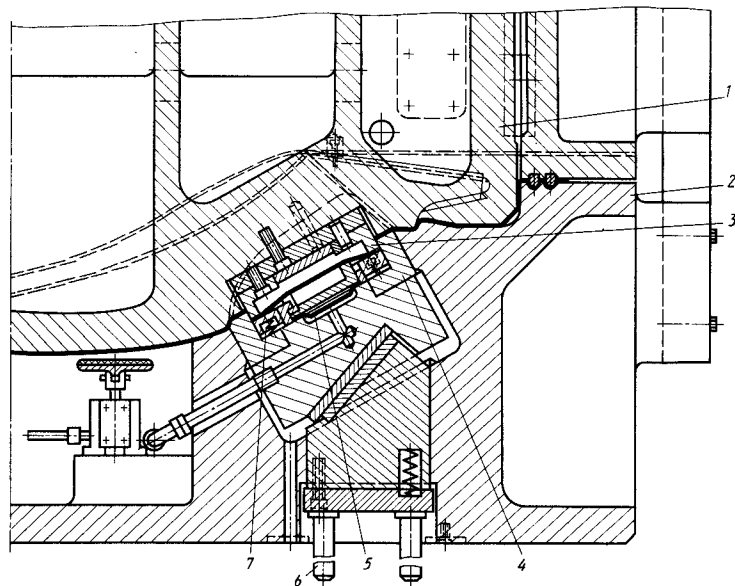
Разрез конструкции штампа для выполнения вытяжки основной формы облицовочной детали и дополнительной вытяжки с применением пресса тройного действия
